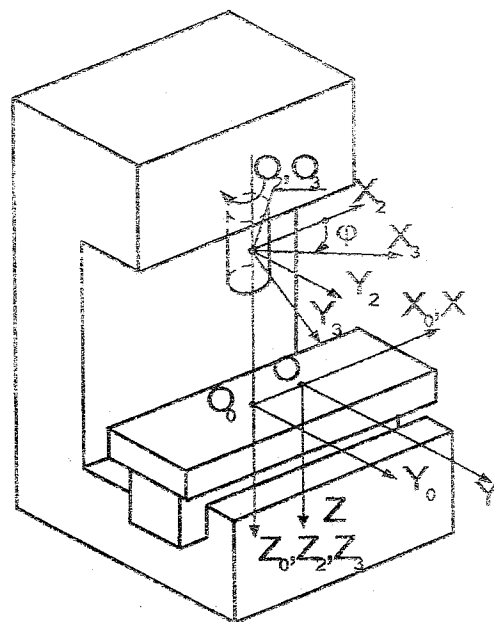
Формообразующая система вертикально-фрезерного станка: системы координат: S_0 – обрабатываемой детали со столом; S_1 – продольных салазок; S_2 – станины; S_3 – шпинделя
